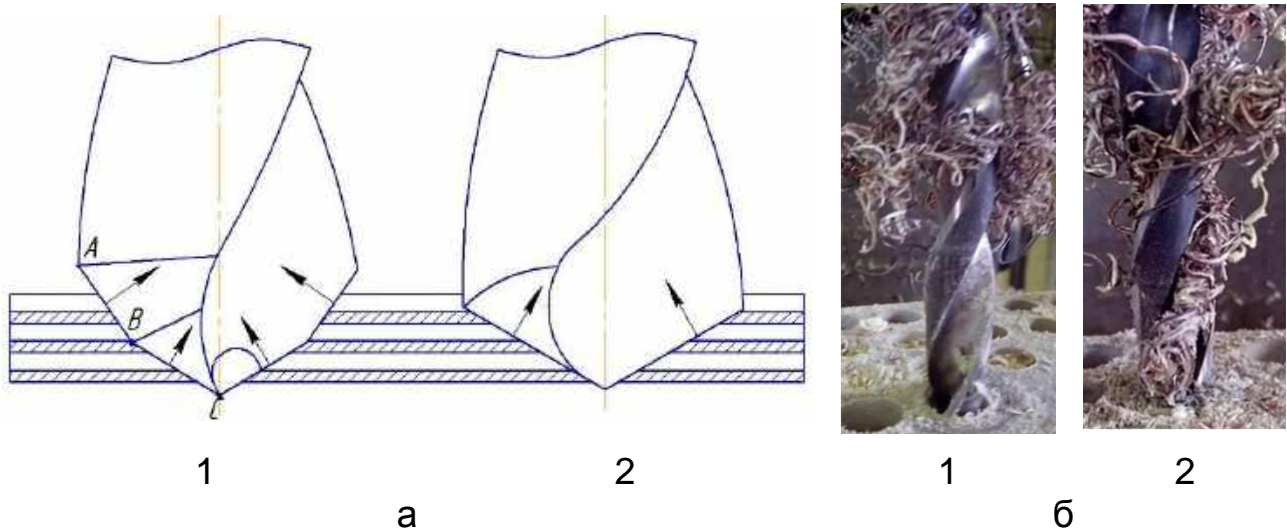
Схема руху (а) та загальний вигляд (б) стружки залежно від форми заточування різальної частини свердла: 1 – П; 2 – Н
